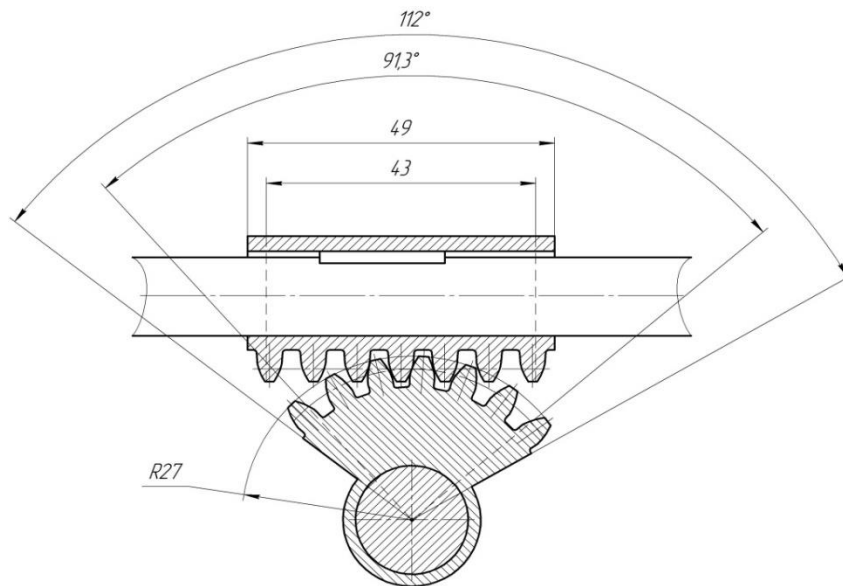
Механізм переключення блоків коробки швидкостей з двома зубчатыми колесами
